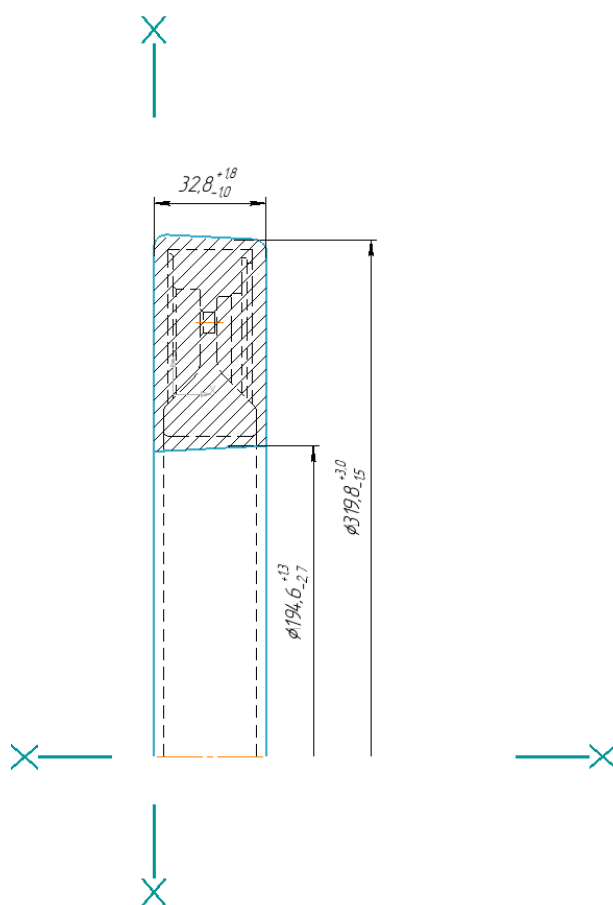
Ескіз заготовки при виготовленні на ГKM
